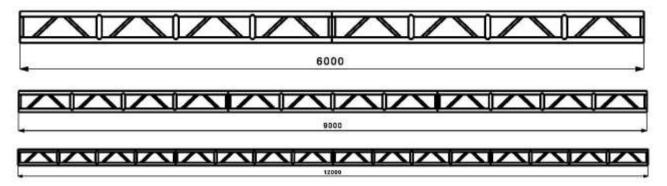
Desde arriba hacia abajo: viga de 6 m obtenida mediante la unión de 2 vigas TR443AL1-00-00; viga de 9 m obtenida mediante la unión de 3 vigas TR443AL1-00-00; viga de 12 m obtenida mediante la unión de 4 vigas TR443AL1-00-00.
